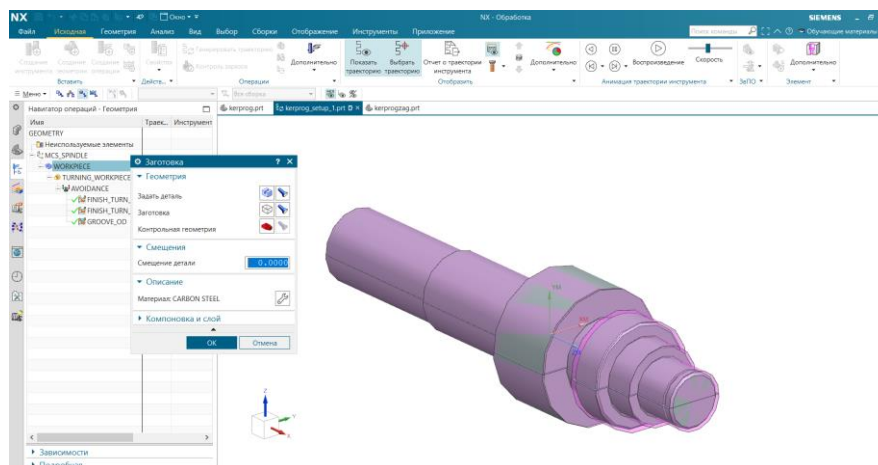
Визначення деталі, заготовки в системі NX CAM
